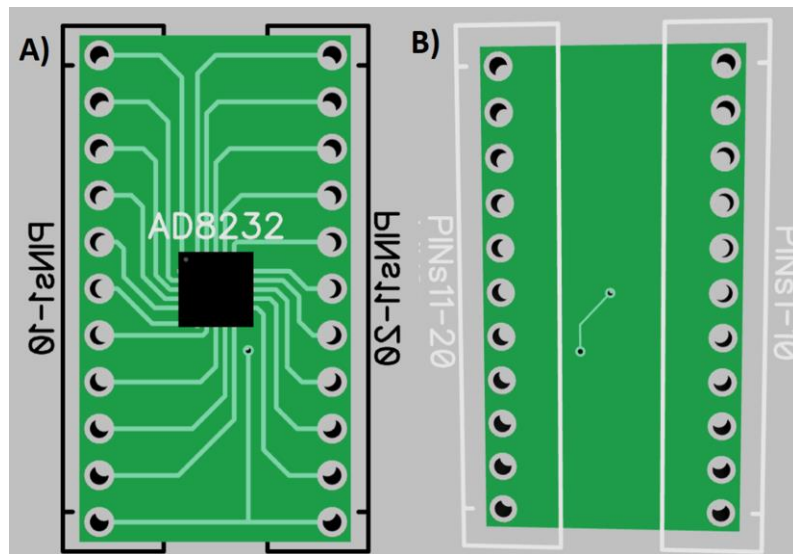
Vista 3D del Adaptador SMD-DIP en PCB del chip AD8232
